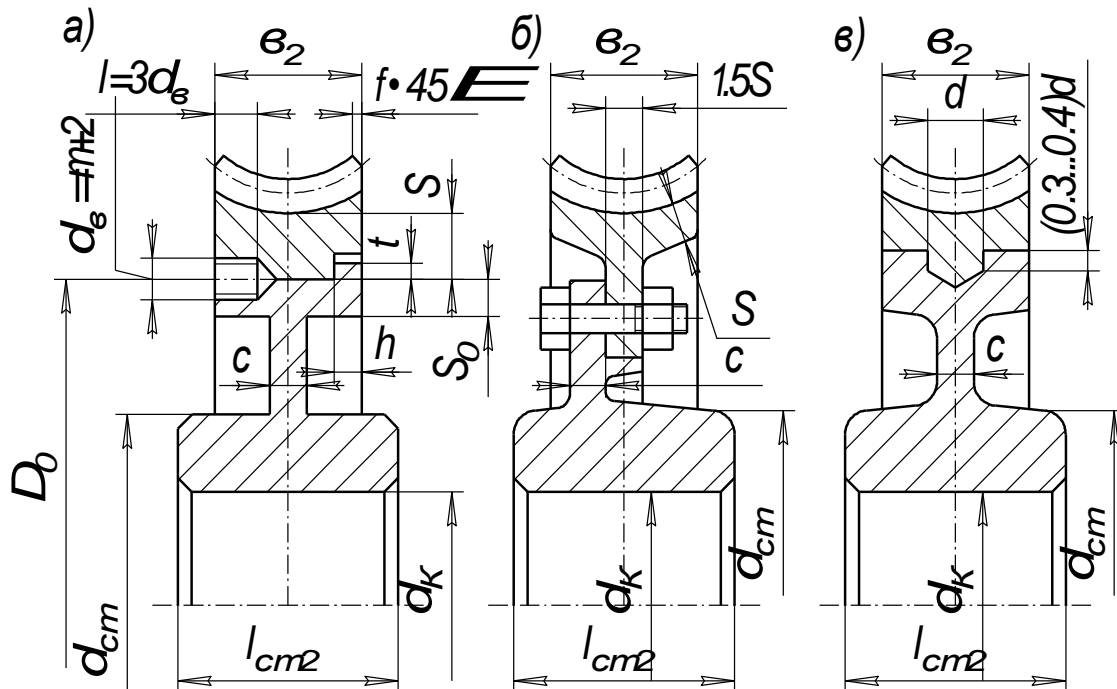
Конструкции составных червячных колёс, образованных соединением зубчатого венца с центром: а – посадкой с натягом; б – болтами, поставленными без зазора; в – заформовкой (наплавленный венец)
